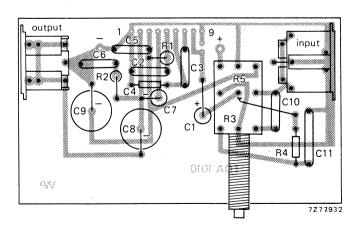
Lo stesso circuito stampato di fig. 10 visto dal lato*componenti.
